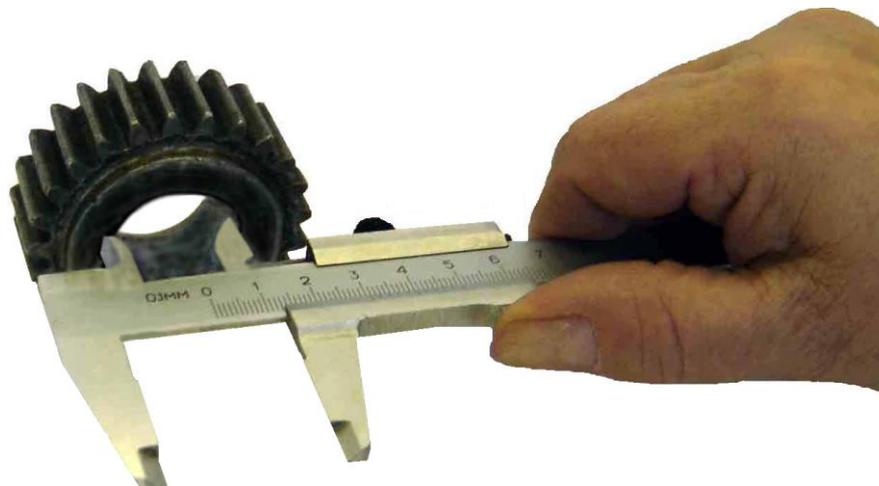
Измерение размера глубины шпоночного паза колеса
